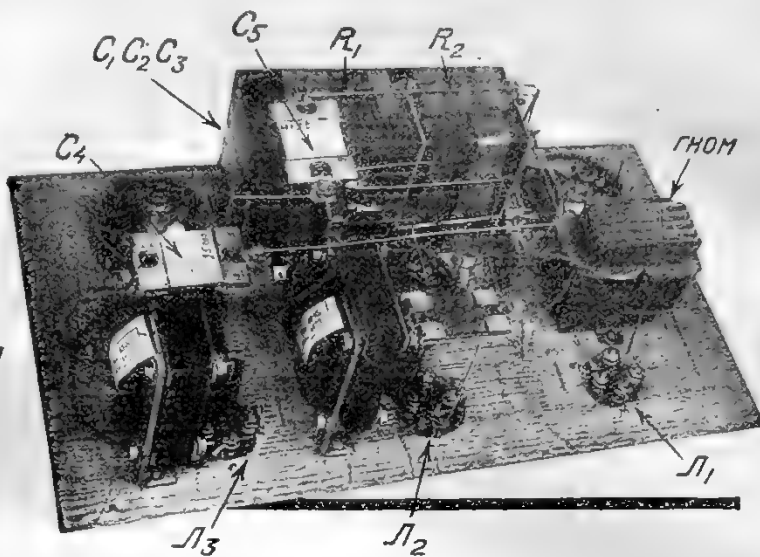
Расположение деталей и вид монтажа выпрямителя и усилителя.
